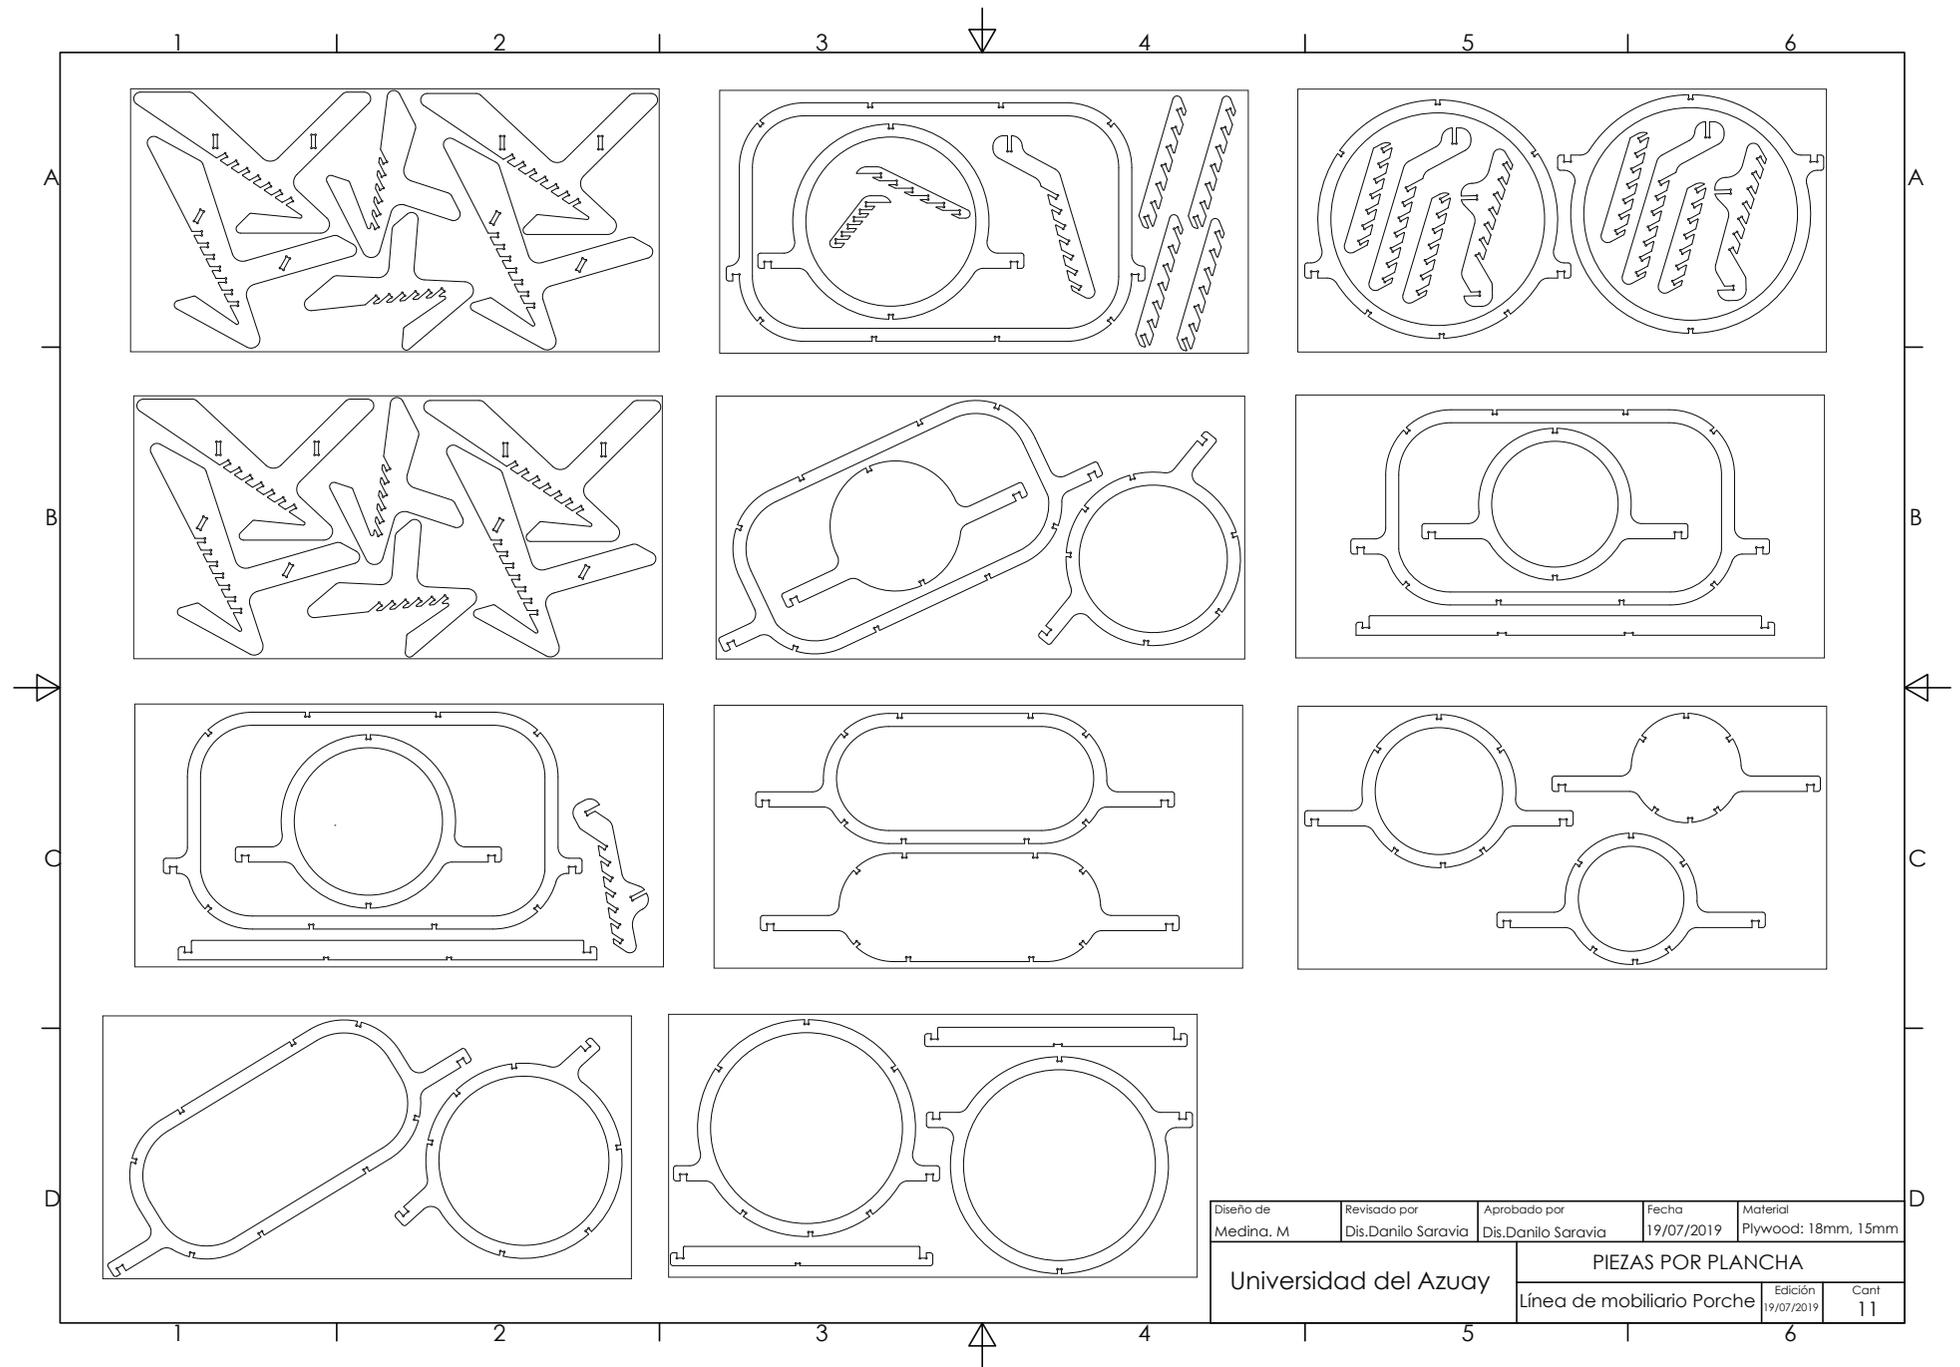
Piezas por Plancha-Plywood 18mm-15mm
